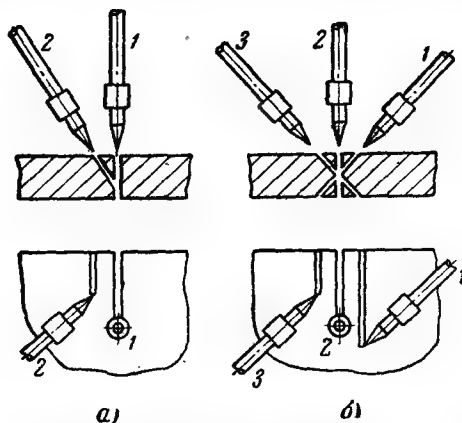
Схема одновременной резки и обработки кромок блоками резаков.
